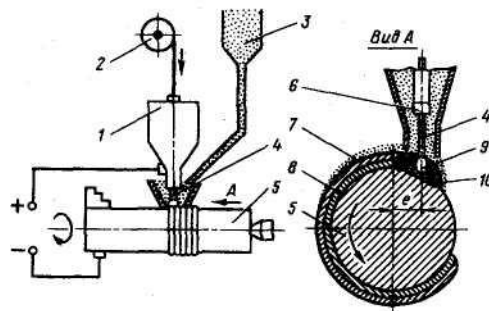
Схема электродуговой наплавки детали под флюсом:
